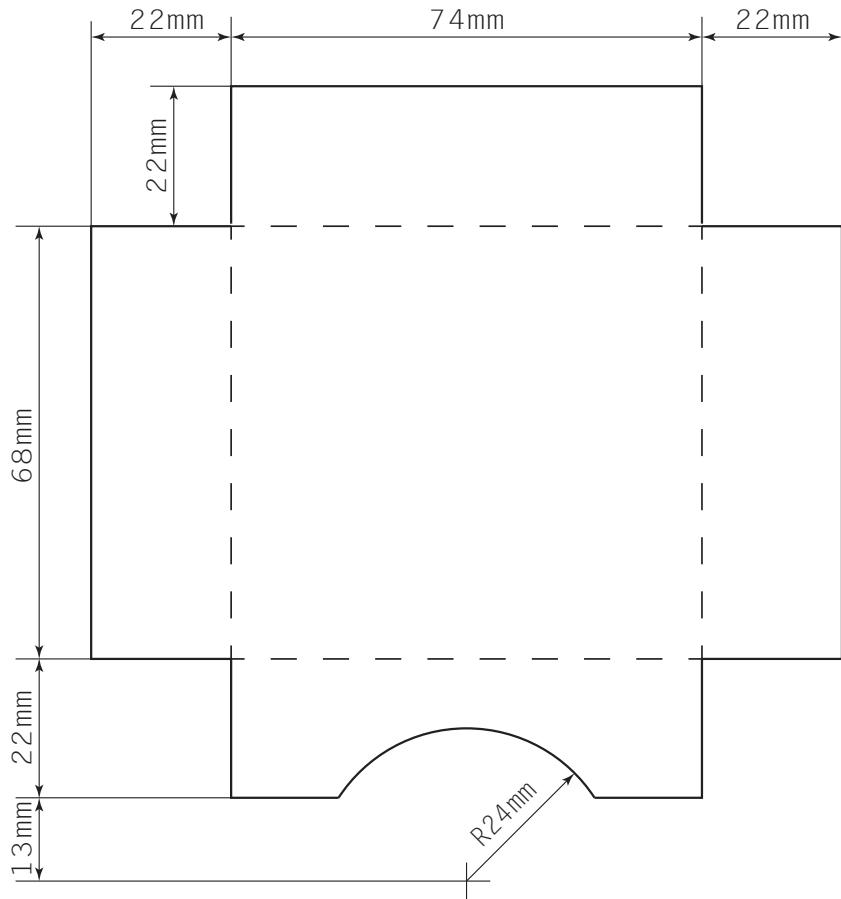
DISEÑO DEL CORTE DE LA CUBIERTA DEL MÓDULO EXTERIOR (TAPA)
